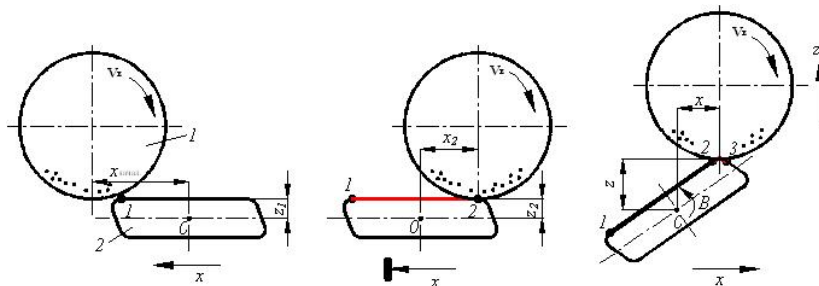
Покадровое перемещение инструмента и заготовки при формировании наружного контура хвостовика (начало)
